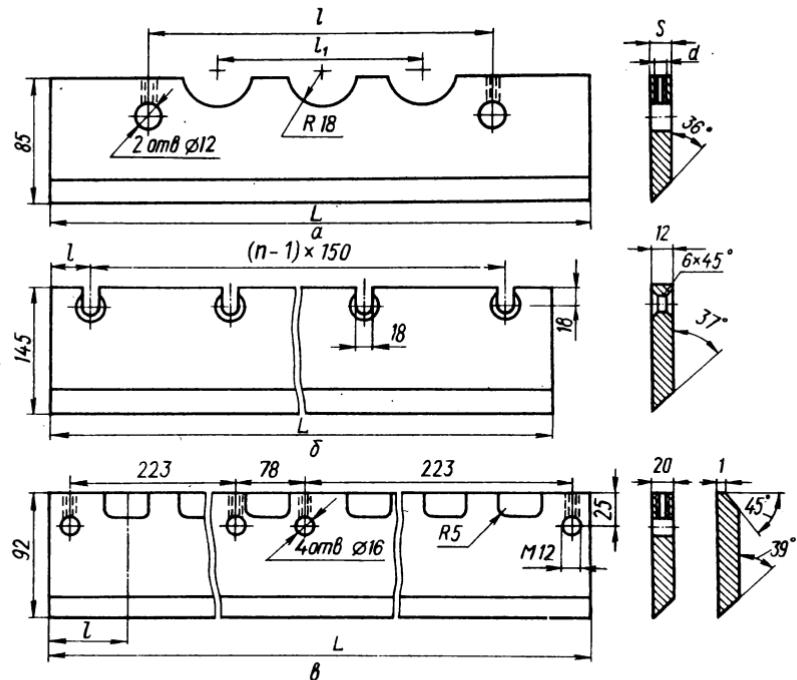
Рубильные ножи рубительных машин с регулировкой установочной ширины:
